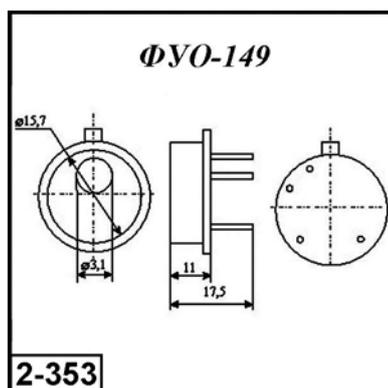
Внешний вид и габаритные размеры ФПУ ФУО-149
